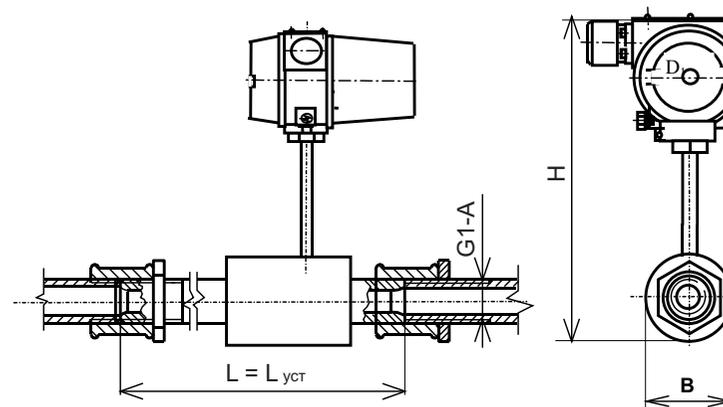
Установочные размеры преобразователя исполнения В типоразмера Ду 25 мм
